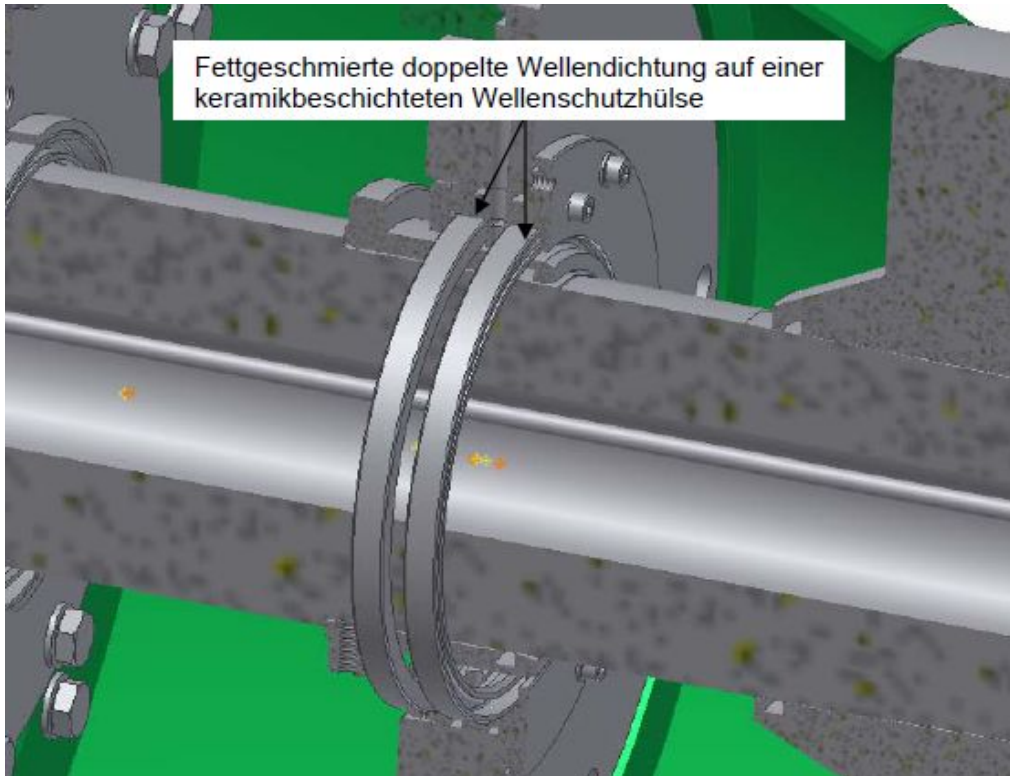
doppelte Wellendichtung auf keramikbeschichteter Wellenschutzhülse
